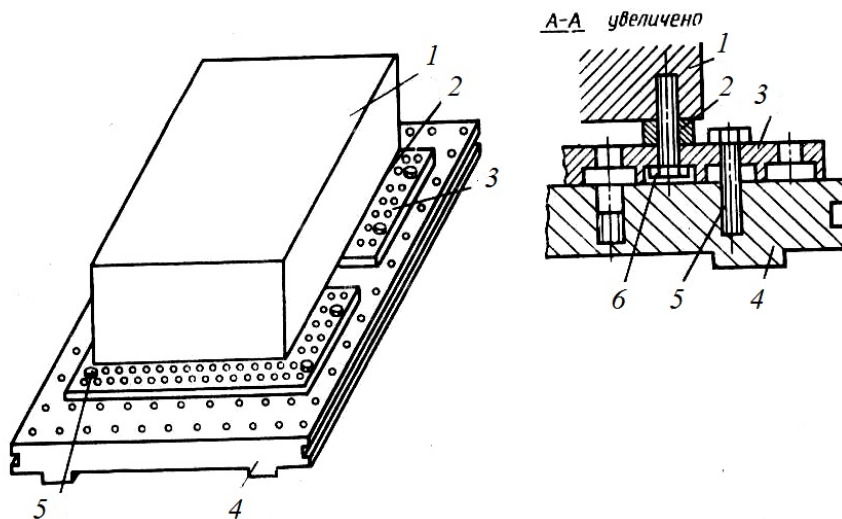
Схема закрепления заготовки с ложными пластиками:
